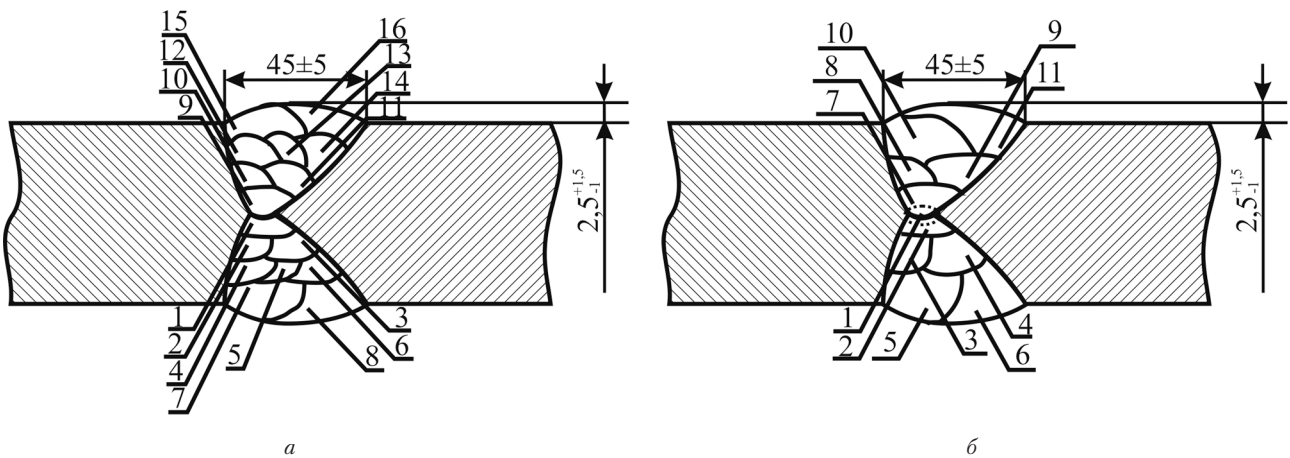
Эскизы опытных сварных соединений с указанием порядка проходов:
